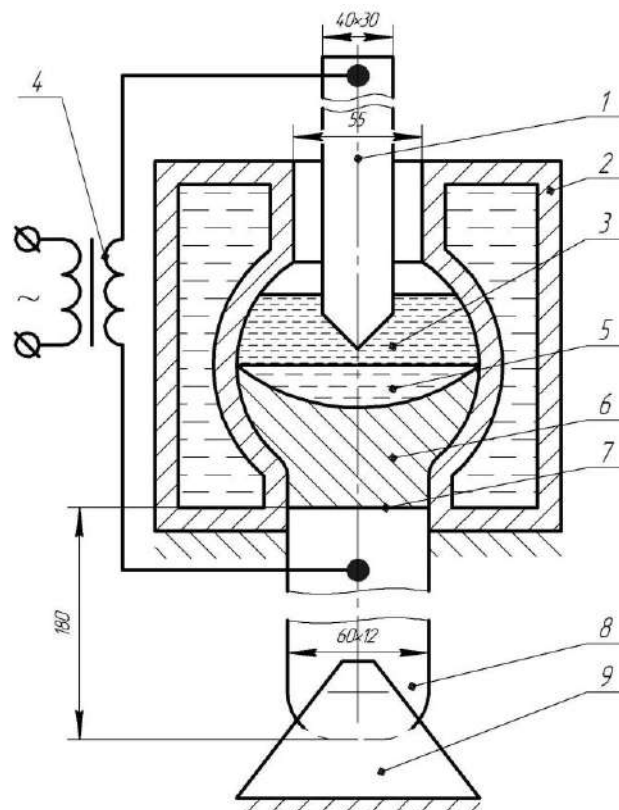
Схема процесу ЕШН: 1 – електрод, який витрачається; 2 – кристалізатор; 3 – шлакова ванна; 4 – джерело живлення; 5 – металева ванна; 6 – наплавлений метал ударної частини, який закристалізувався; 7 – зона сплавлення ударної частини з хвостовиком; 8 – хвостовик; 9 – фіксатор
